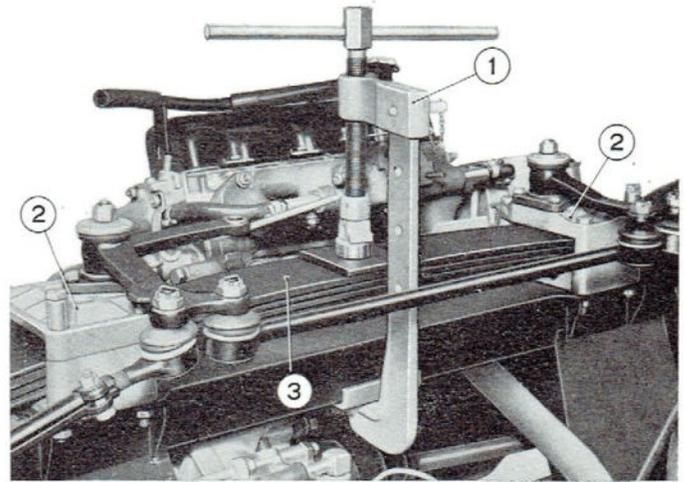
Spanner zum Festspannen der Blattfeder.
